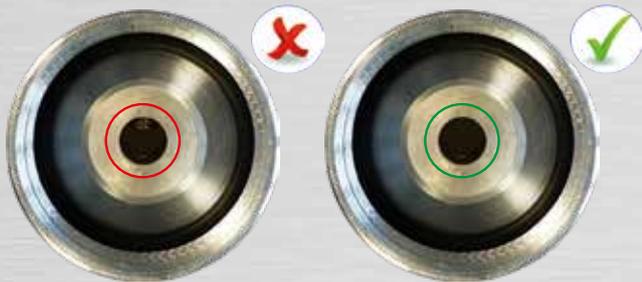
Kontrolle der Dichtung und Zylinderkopfschrauben
